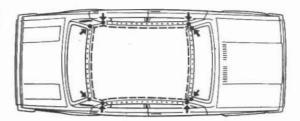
Sitios de soldadura del techo. Con puntos se indican las costuras de soldadura por contacto. Con flechas se indican los sitios de soldadura autósena
